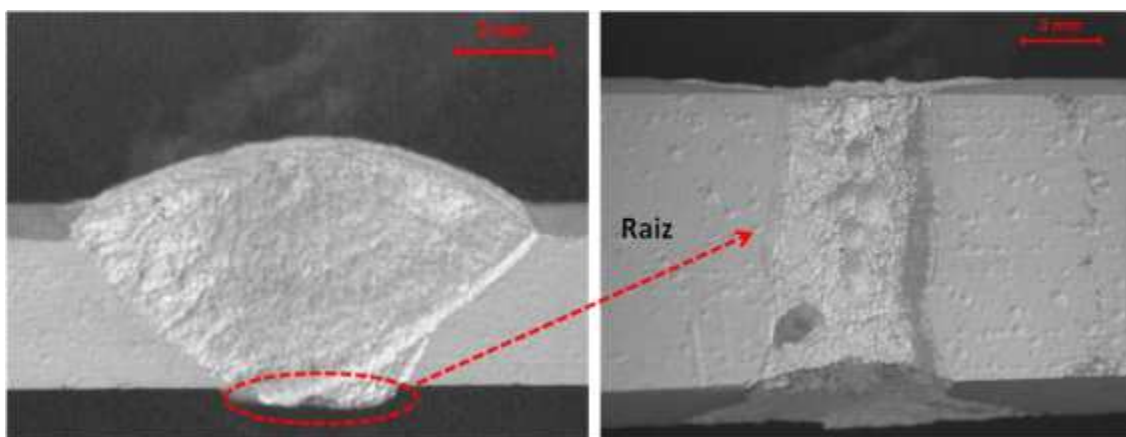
Aspecto macroscópico da raiz da solda, depois do ensaio, corpo de prova com solda – 04. Fonte: Do autor
